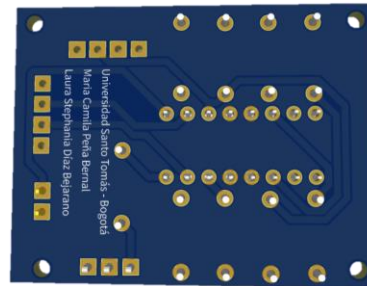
Vista 2D superior del diseño PCB del módulo driver puente H.
